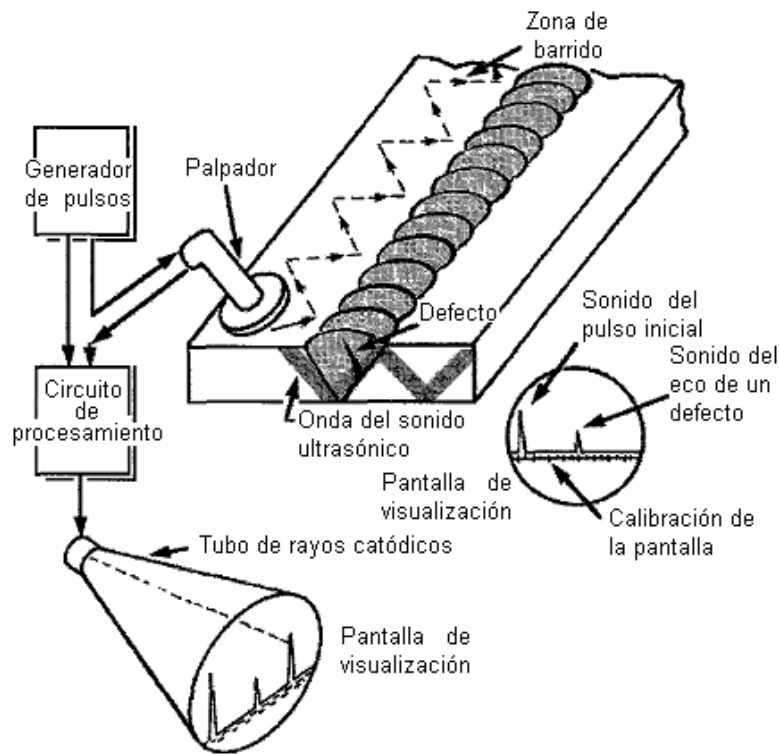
Inspección de uniones soldadas mediante la técnica de ultra sonido
